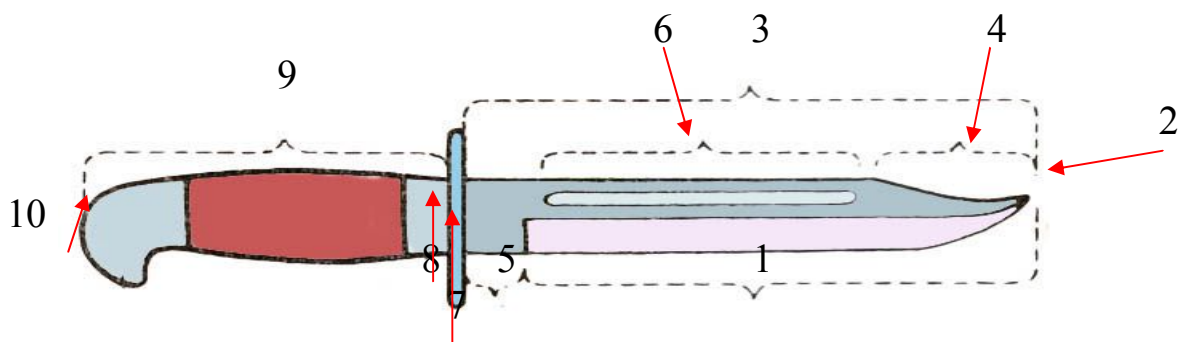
Найменування частин ножа: 1 – лезо; 2 – вістря; 3 – обух; 4 – скіс обуха; 5 – п'ята клинка; 6 – виточка (дола); 7 – обмежувач; 8 – нижнє кільце; 9 – рукоятка; 10 – наконечник (голівка) рукоятки
